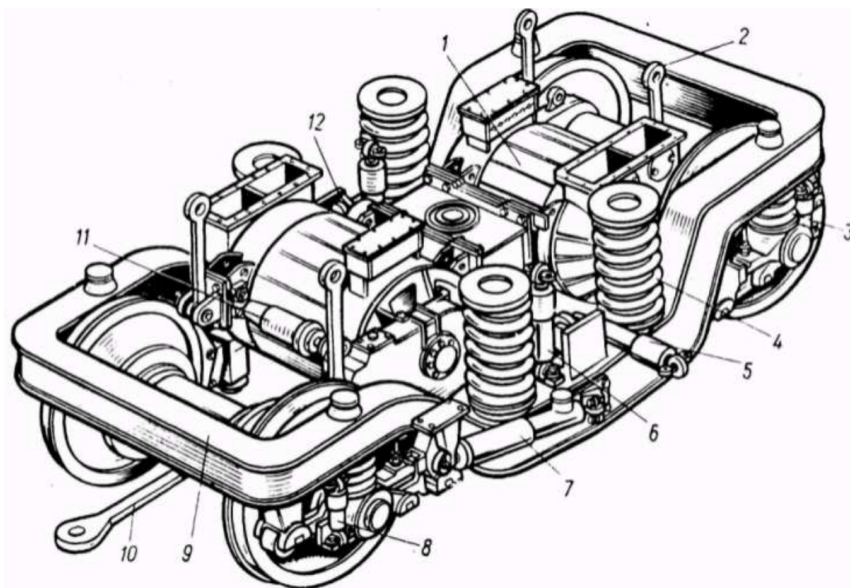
Візок локомотива: 1 – ТЕД (два на кожну пару коліс візка); 2 – підвіска моторно редукторної системи; 3, 4 – пружини; 5, 6 – гідравлічні компенсатори-гасителі коливань кузова; 7, 8 – гідравлічні компенсатори-гасителі коливань візка; 9 – вал тягової муфти; 10 – брус; 11 – пружний механізм; 12 – упор пневмобалона
